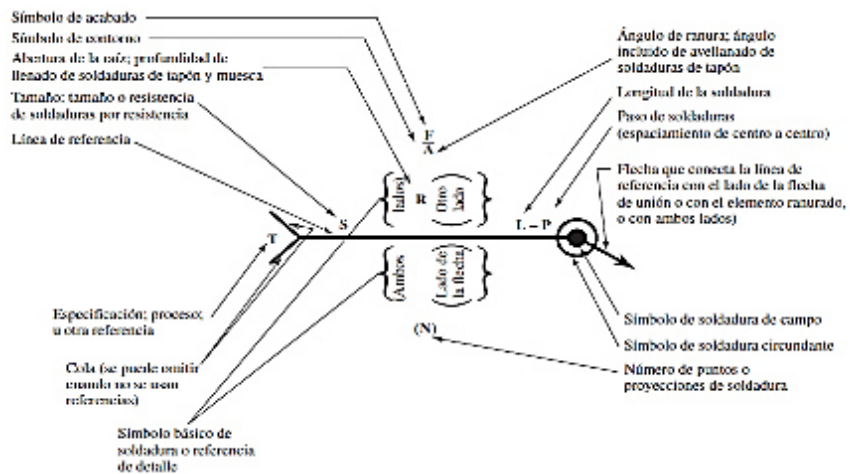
Estructura del símbolo de soldadura. Tomado de “Diseño en Ingeniería Mecánica de Shigley” por Budynas et al. (27 pág. 454)
